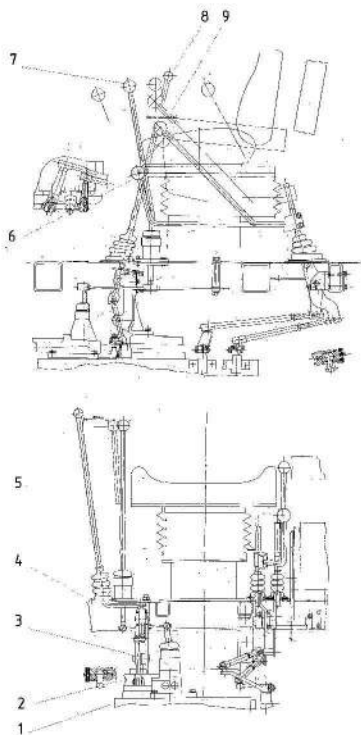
Механическое управление режимами коробки передач: 1 – верхняя половина картера коробки передач; 2 – механизм переключения передач; 3 – кулиса; 4 – полка кабины; 5 – рабочее место водителя; 6 – рычаг управления режимной муфтой раздаточного вала; 7 – рычаг управления режимной муфтой грузового вала и муфтой заднего хода; 8 – рычаг переключения передач; 9 – рычаг управления задним ведущим мостом.
